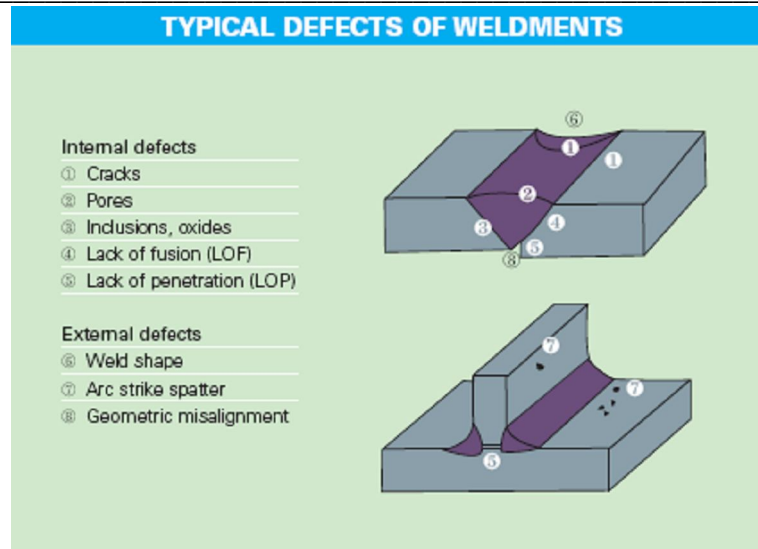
Defeitos típicos nas soldaduras. [38]
